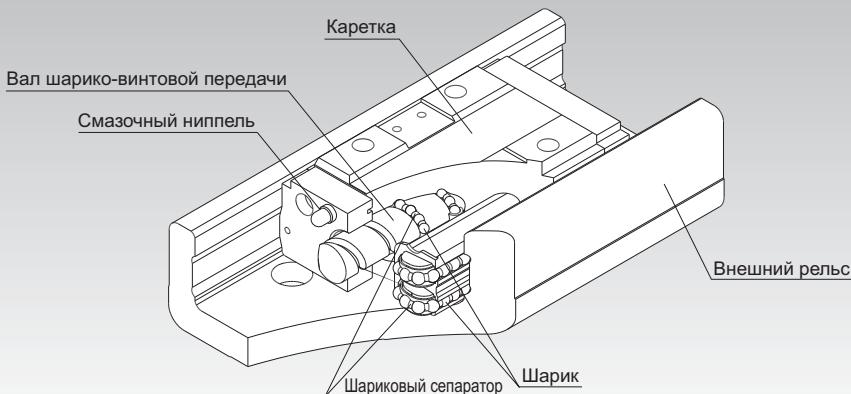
Конструкция шариковой рельсовой направляющей LM модели SKR с сепаратором
